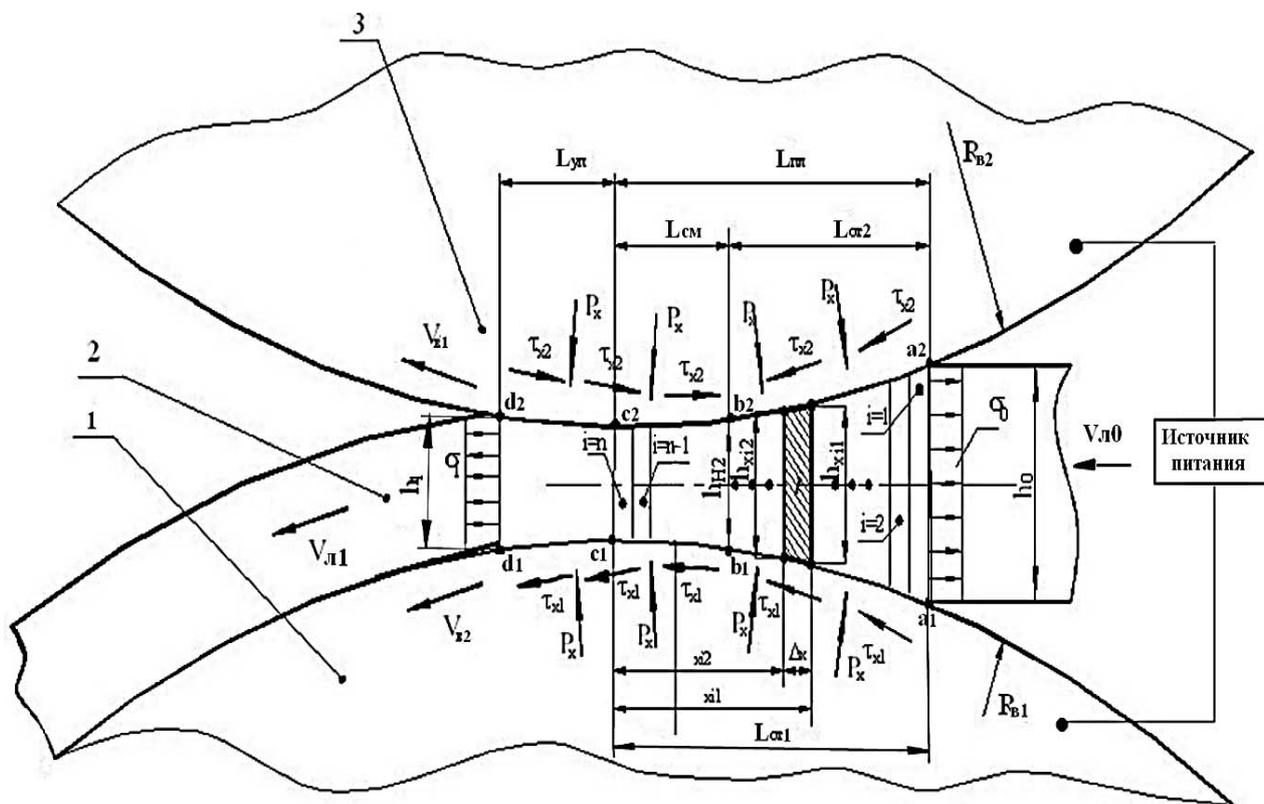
Расчетная схема процесса наплавки цилиндрической детали:
